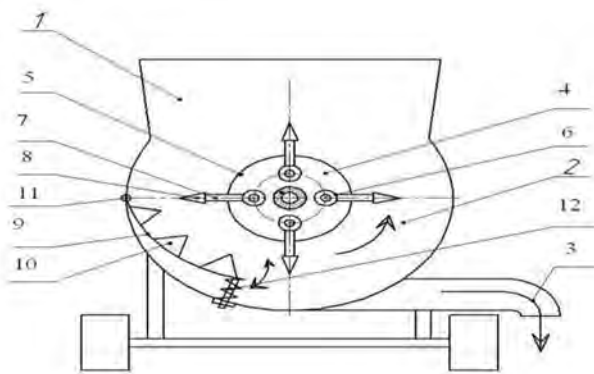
Общий вид кормораздатчика-измельчителя
